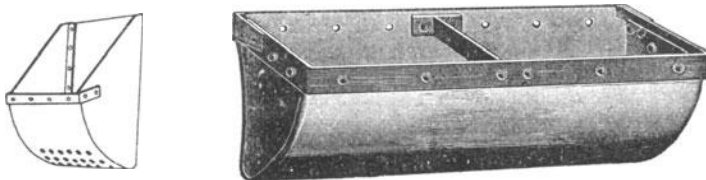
Gelochter Becher. Abb. 271. Becher mit gekrümmter Rückwand.
